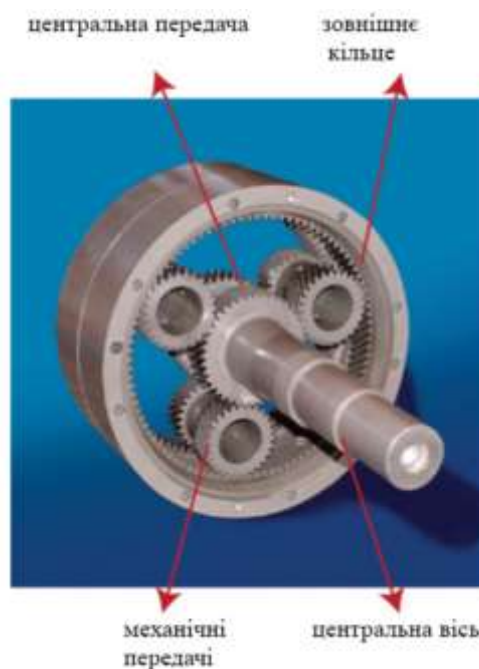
Внутрішній механізм планетарного редуктора швидкості
